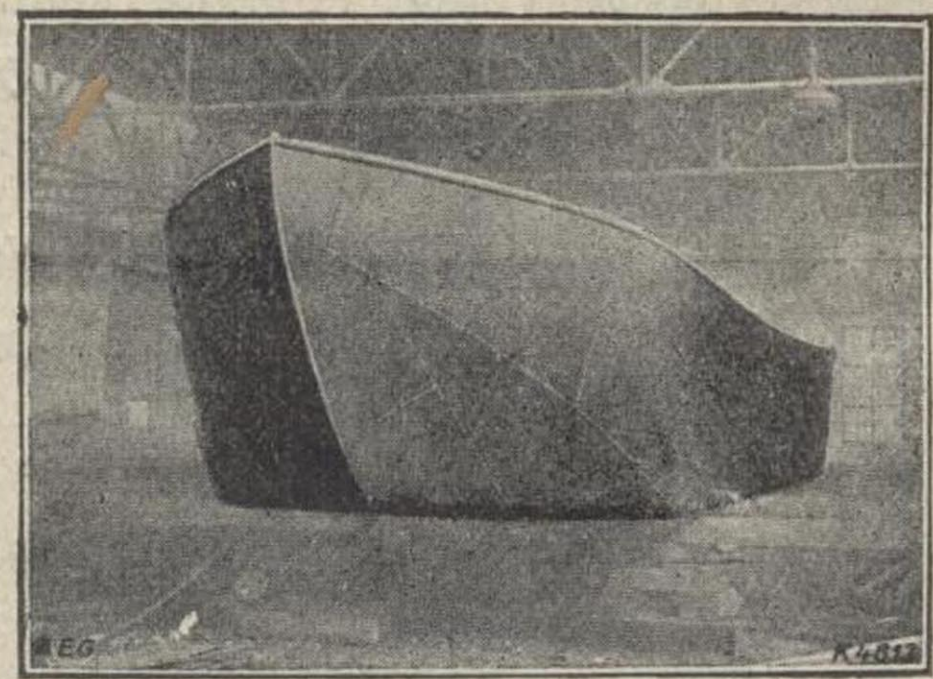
Vista exterior del casco soldado de una barcaza.
